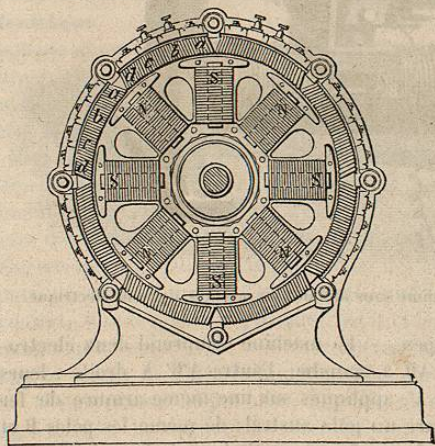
Disposition de la machine de Gramme à courants alternatifs.
